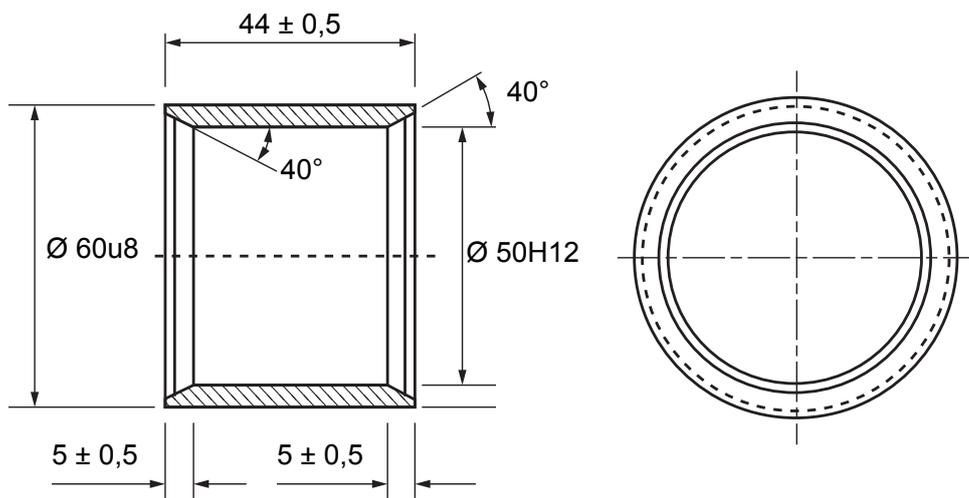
Bucha rígida para ponteira do tipo olhal da classe D50-C
